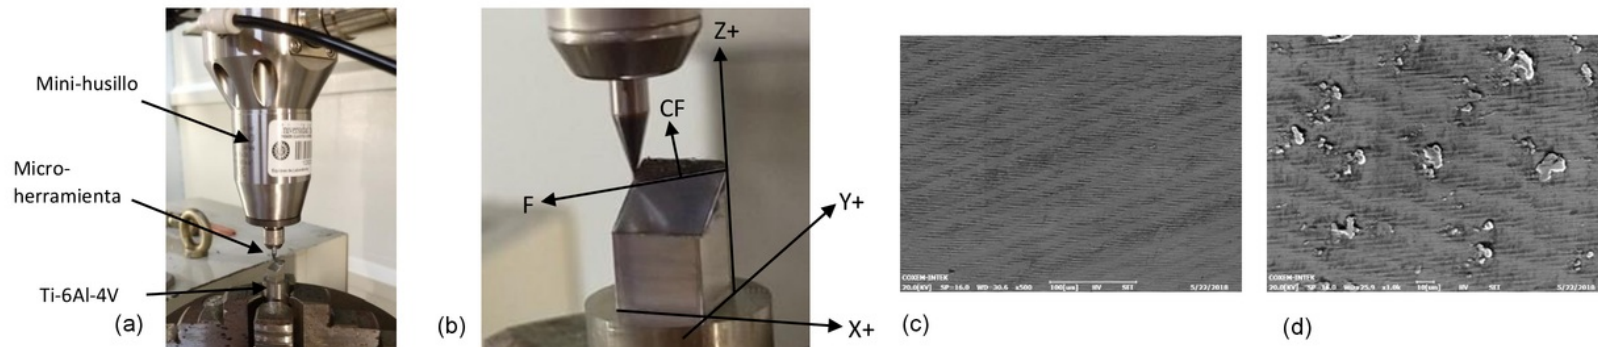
(a). Montaje de micromaquinado en centro de mecanizado vertical. (b) Prueba experimental de micro-maquinado concordante (c) Defecto *smeared/adhered material* ocasionado por el maquinado discordante. (d) Maquinado concordante; no se presenta el defecto. Fuente: Autores
